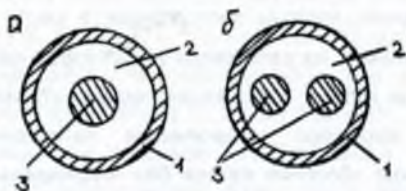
Вид поперечного сечения заготовки: 1 - ободочка; 2 - изоляционный порошок; 3 - сердечник.
